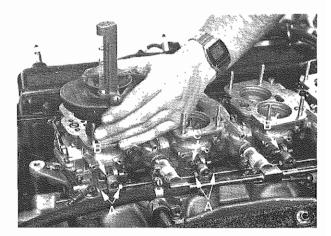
A - Dadi regolazione tirante Nuts, throttle rod control
